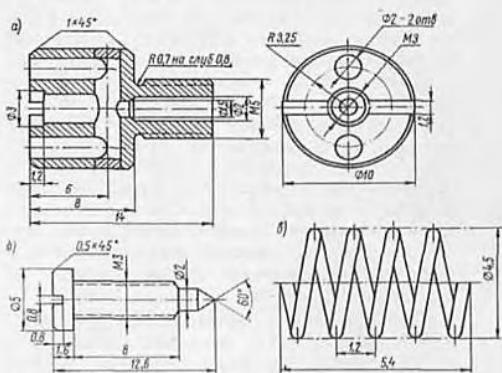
Устройство, регулирующее главный воздушный жиклер: а — корпус; б — регулировочный винт; в — пружина.
